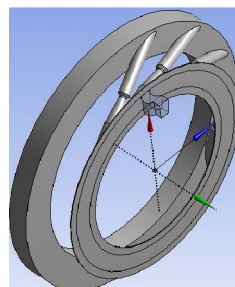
Булева операция пересечения - получения канала РК для одной лопатки
